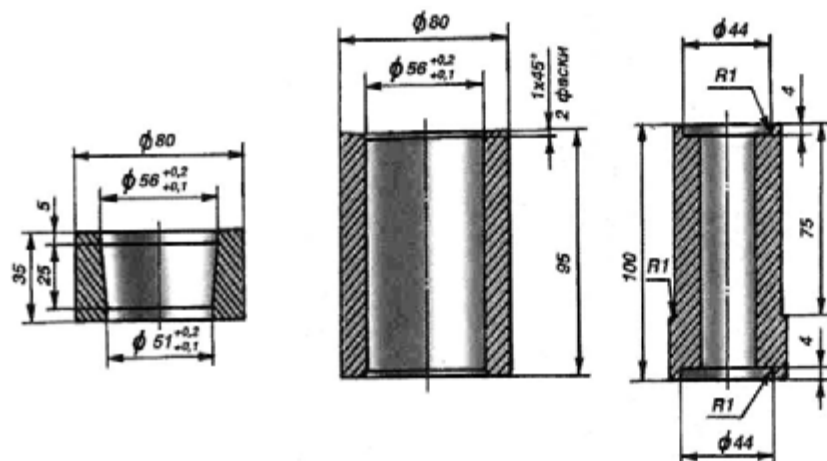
Оправки для запрессовки резинометаллических шарниров в ушко рессоры и кронштейны.
